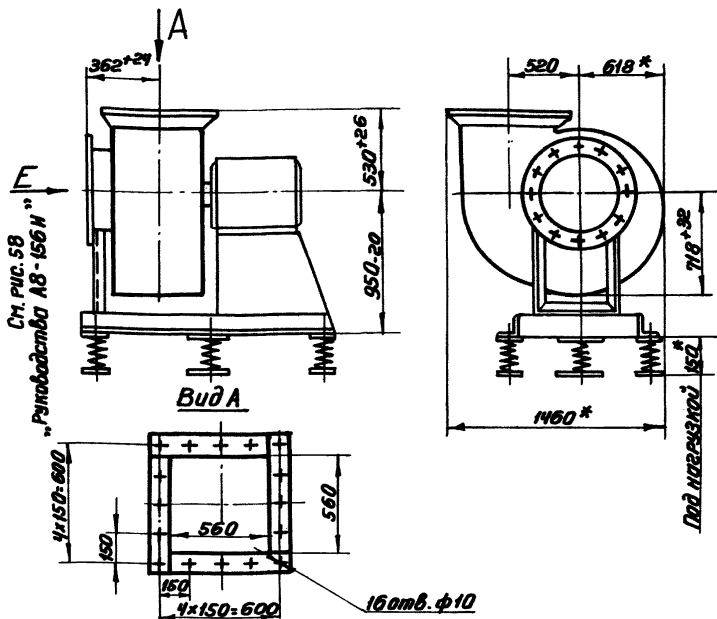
Основные присоединительные и установочные размеры вентиляторов Ц4-70 с промежуточными диаметрами колес № 2,5 - 6,3 (исполнение I)
